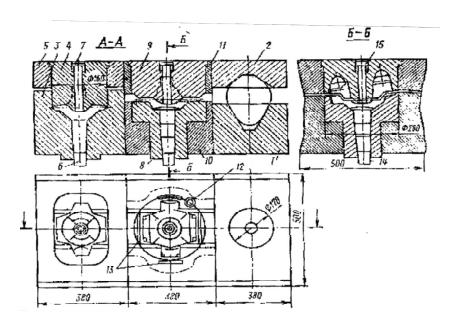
Схема комплекта ручьевых вставок для выдавливания крупной поковки поворотного кулака на кривошипном горячештамповочном прессе:
